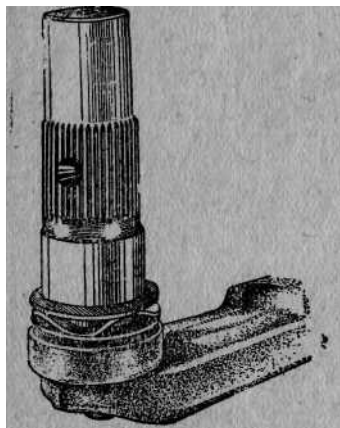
Приспособление для выпressовки и запрессовки кривошипа передней подвески:
